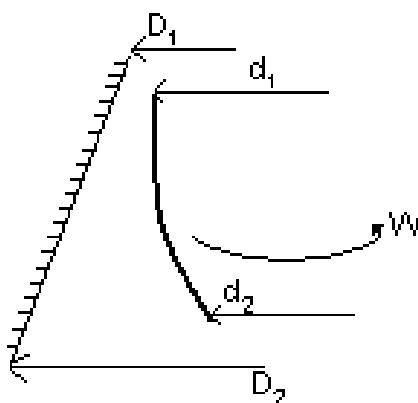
Конструкція з конічною формою твірної кожуха та параболічною формою твірної шнека
